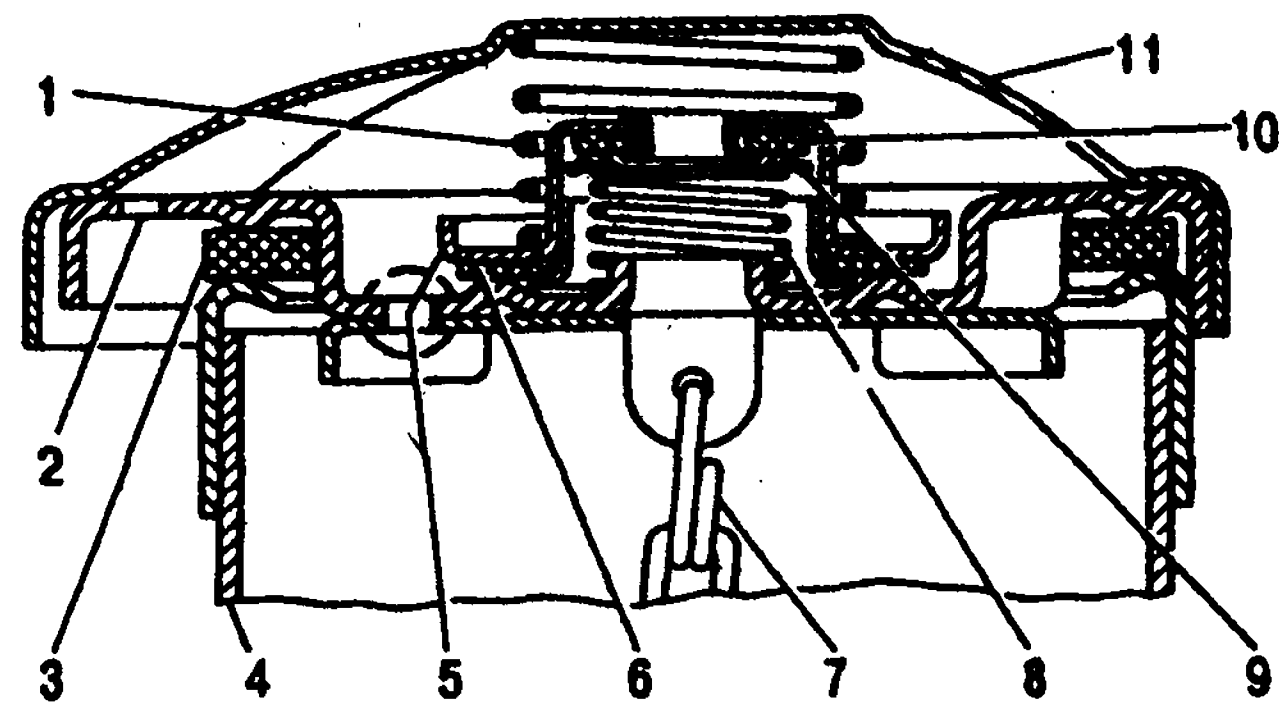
Пробка наливной горловины: 1 и 8 - пружины клапанов; 2 - отверстие сообщения с атмосферой; 3, 6 и 10 - прокладки; 4 - наливной патрубок; 5 - выпускной клапан; 7 - предохранительная цепочка; 9 - впускной клапан; 11 - крышка
